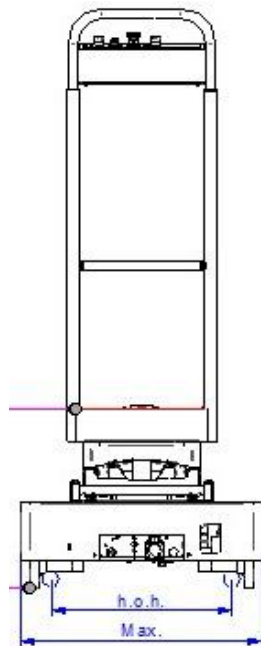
; Dimensions de la largeur en mm, 2 pantographes
